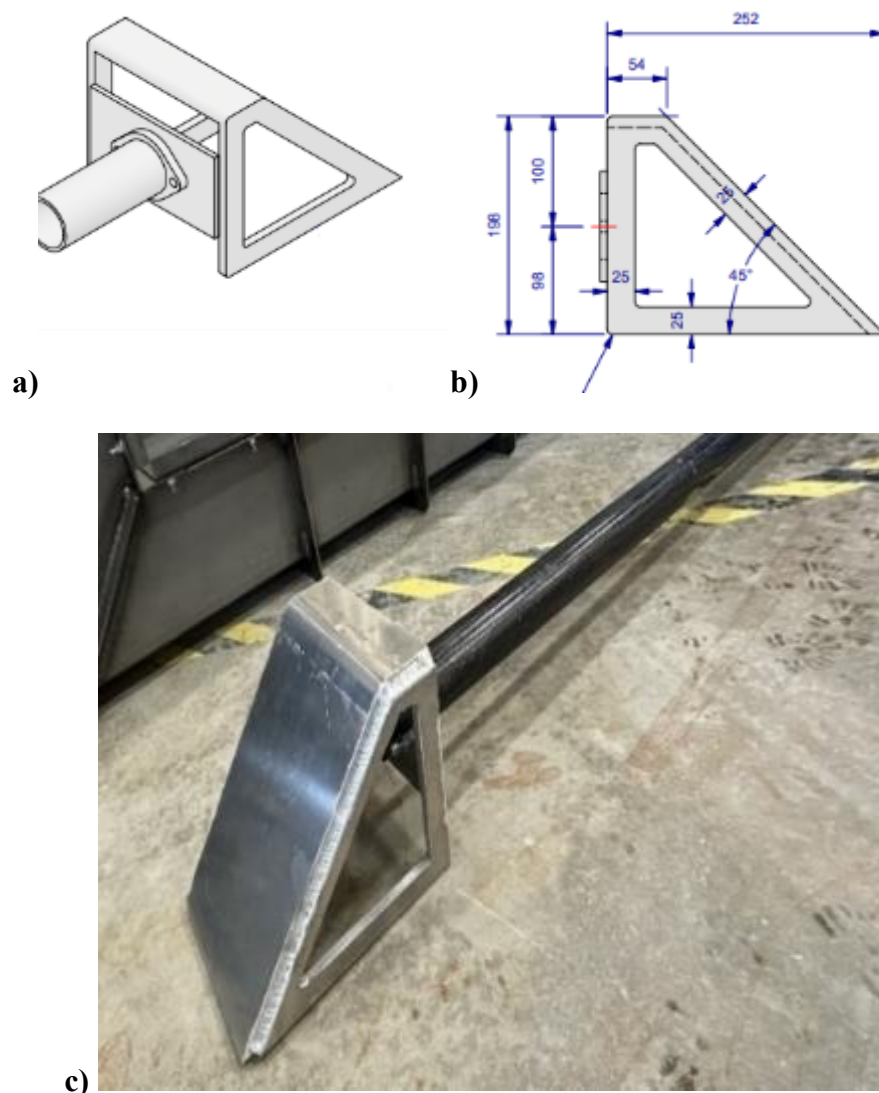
Géométrie de la barricade : a) vue tridimensionnelle, b) schéma avec les dimensions, c) photo de la barricade réelle utilisée pour les essais finaux
